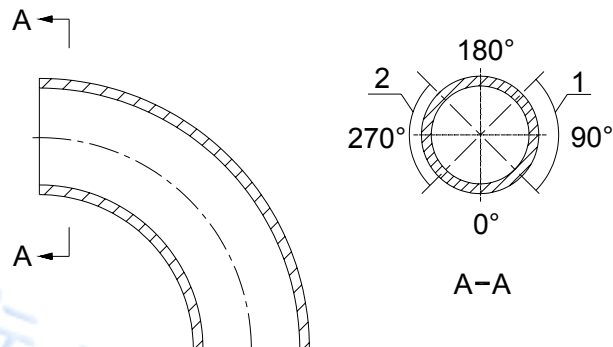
焊接弯头纵向焊缝拼接位置图
